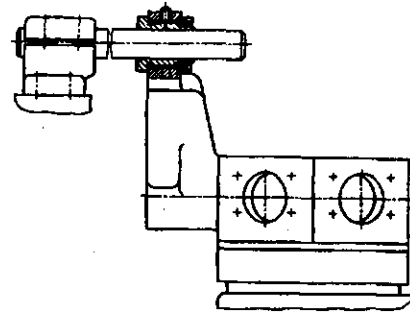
Схема центрирования револьверной головки направляющей штангой
